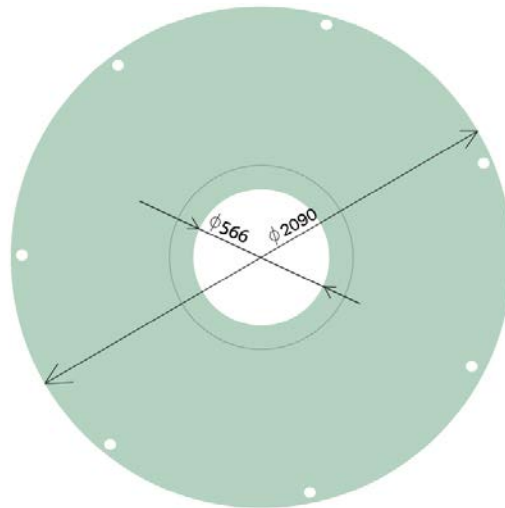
desarrollo de la parte superior de la tela. Vista de planta.
